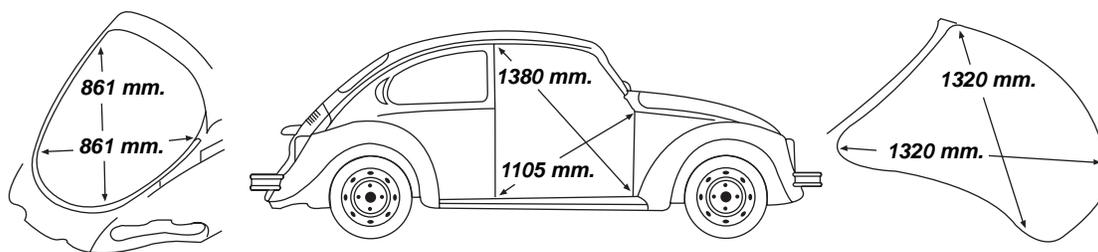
Dimensiones de huecos en tapa motor, cofre y puerta
